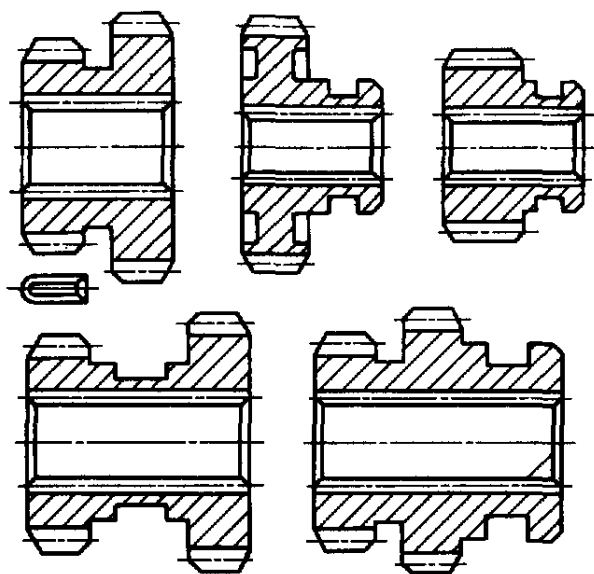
Блоки шестерен и передвижные шестерни
